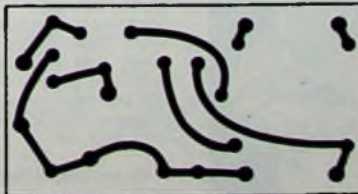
Printzeichnung der Platine (Maßstab 1:1)
